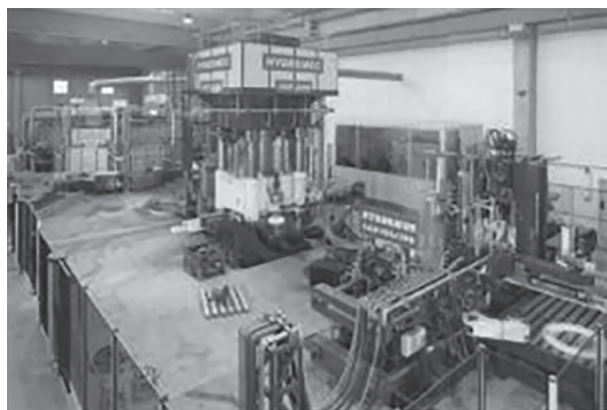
Кольцераскатный стан для колец диаметром до 7000 мм
